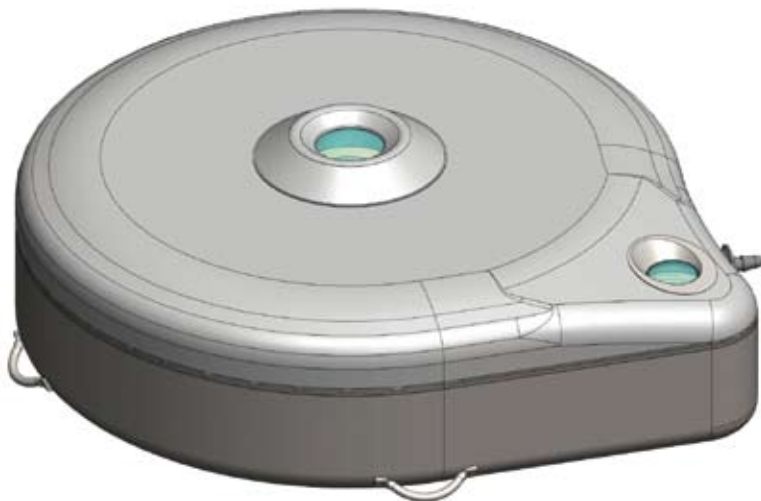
CAD-Design der steuerbaren Schmerzpumpe (Firma Tricumed Medizintechnik GmbH, Kiel)
